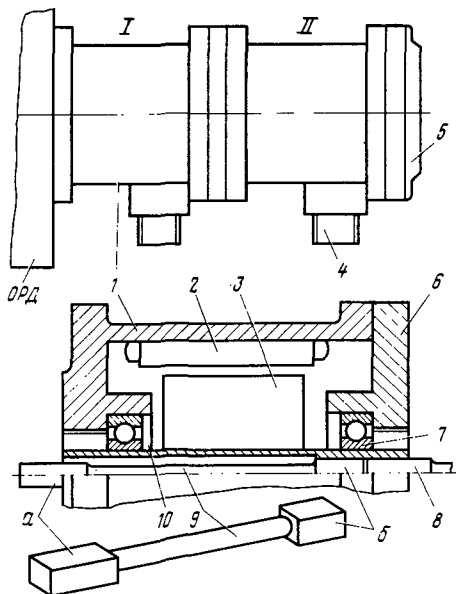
Блок датчиков тахометра: 1 — корпус; 2 — статор с обмоткой; 3 — ротор; 4 — штепсельный разъем; 5 — пластинка; 6 — крышка; 7 — шариковый подшипник; 8, 9 — стержни; 10 — полый вал; ОРД — объединенный регулятор дизеля
